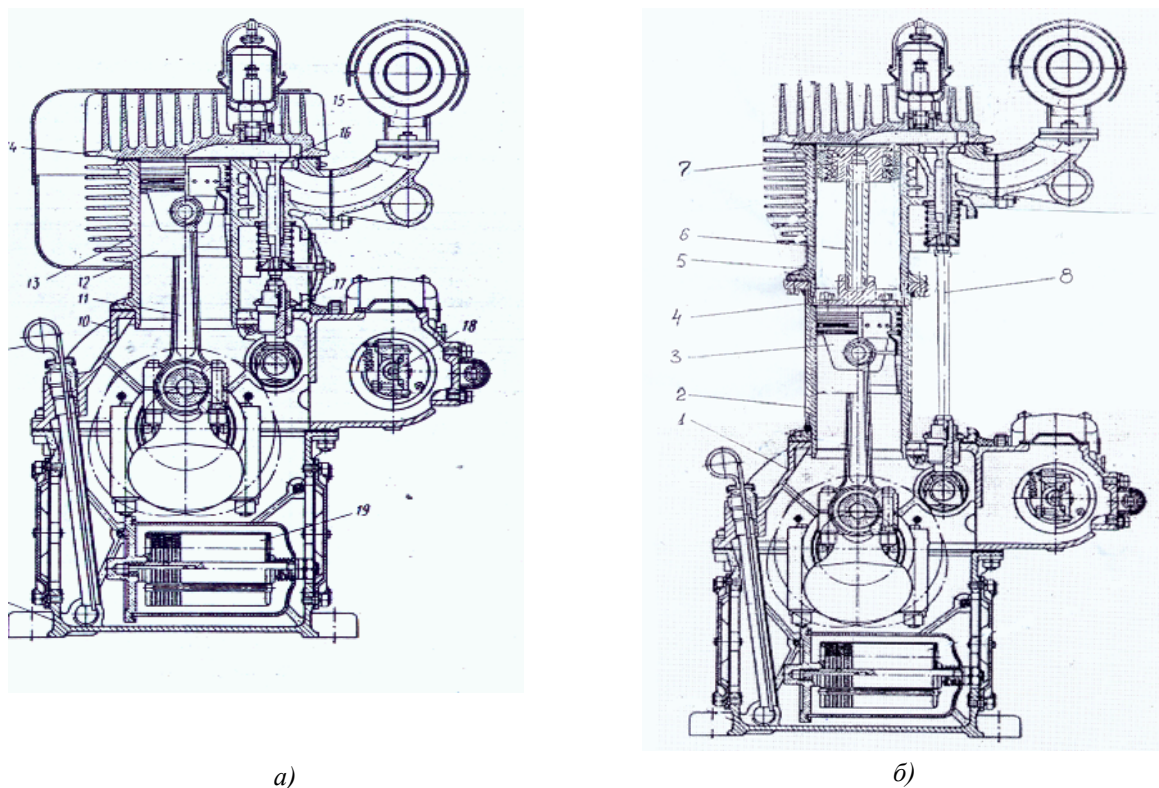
Схемы двигателя для испытаний сухого уплотнения
